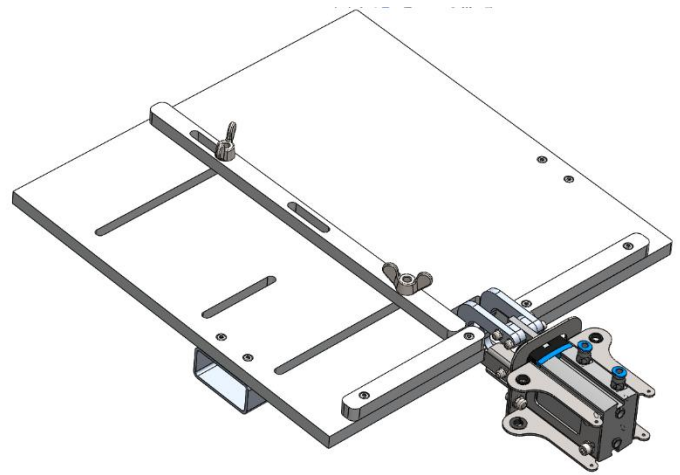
Exploded view en geassembleerd grijperonderdeel
